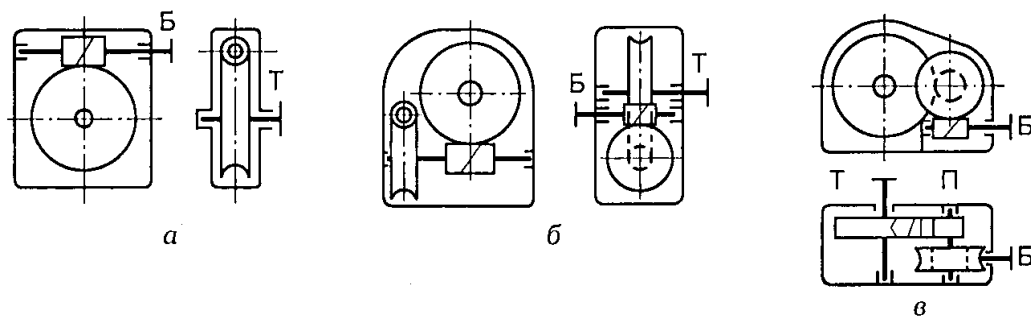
Схемы червячных редукторов: а — одноступенчатый; б — двухступенчатый; в — червячно-цилиндрический
